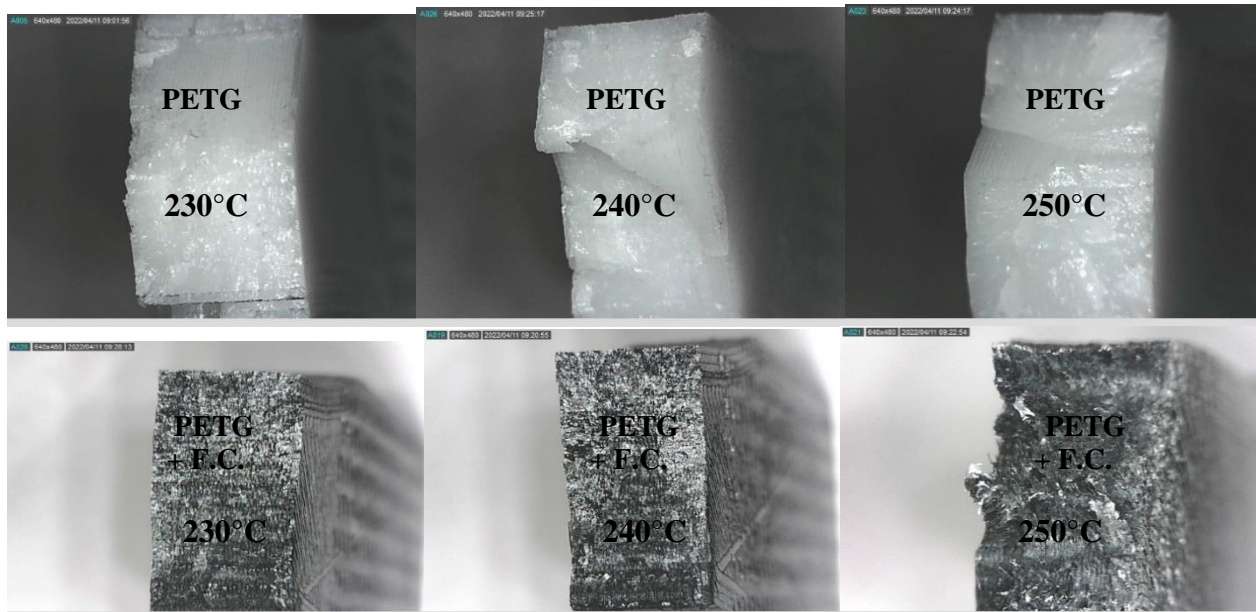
Imágenes SEM de probetas fracturadas de tensión. Fuente: Autor
